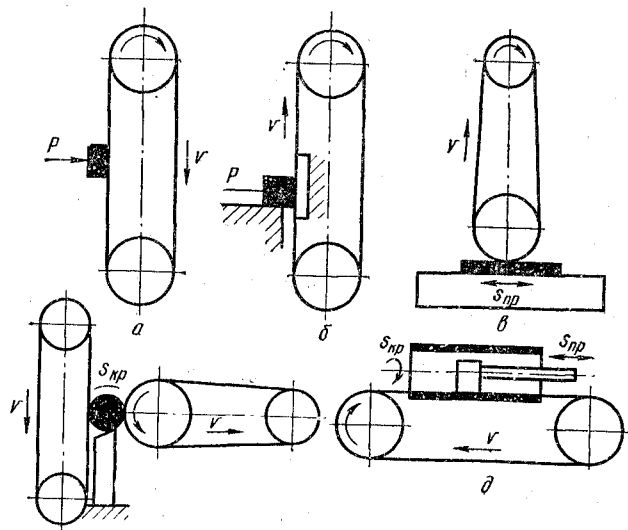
Схемы ленточного шлифования и полирования поверхностей заготовок
